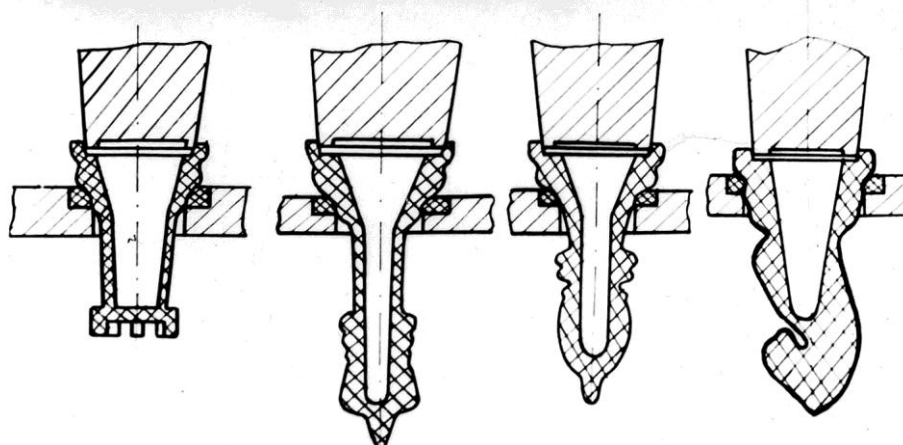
Схема ультразвуковой сварки шахматных фигур
